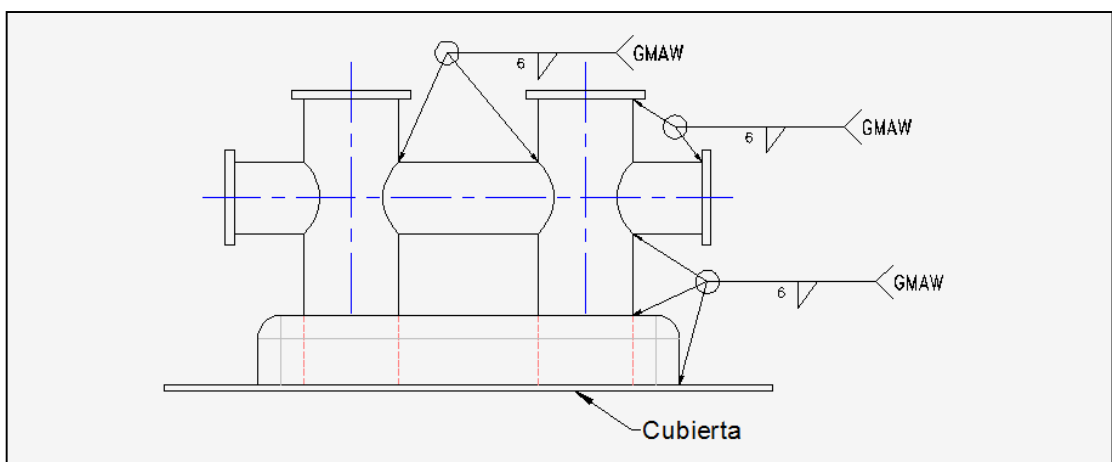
Vista frontal, detalle de soldadura de la bita.
